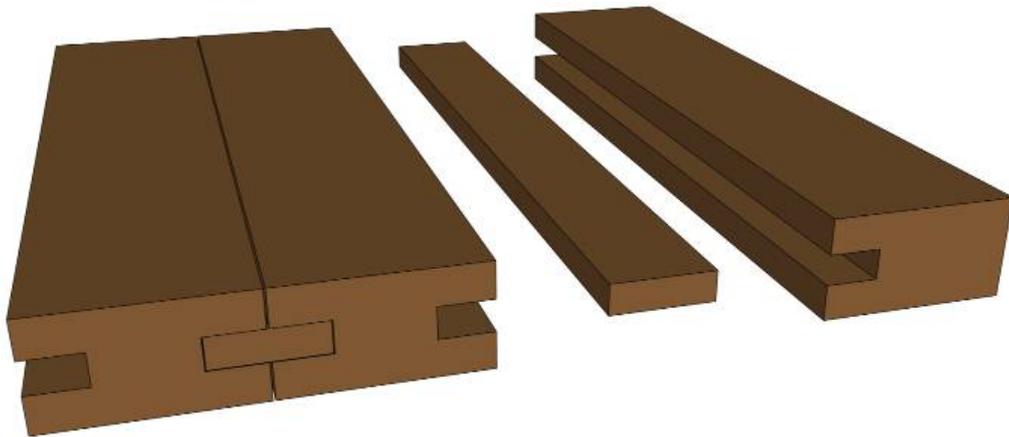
Desenho de construção de tampo de mesa em esquema de fêmeas e chaveta corrida.
